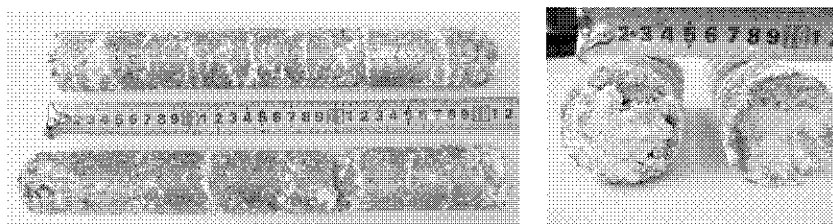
Внешний вид блоков, прессованных из смеси титановой губки и порошка оксида титана
